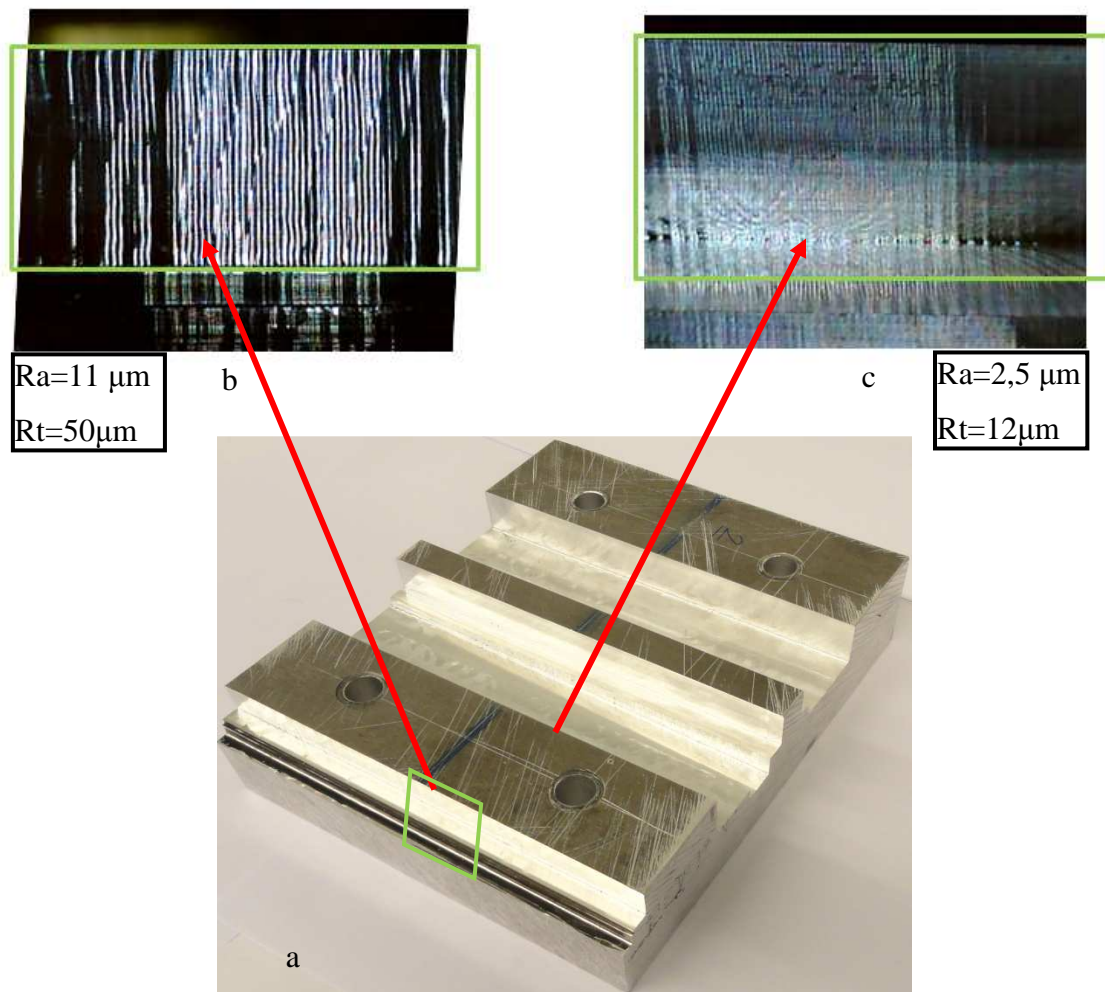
a) Pièce à usiner b) Surface usinée de la tâche 2 c) Surface usinée de la tâche 1
